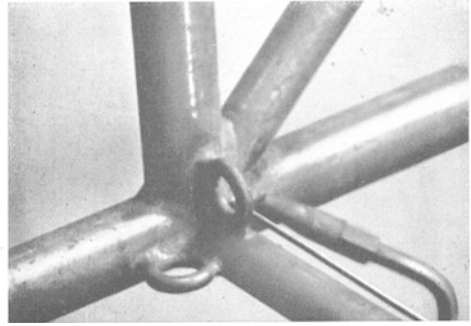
Geschweißter Stahlrohrknotenpunkt.
